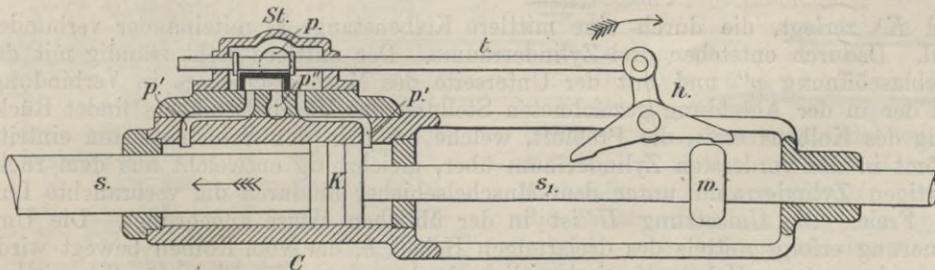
Prinzipskizze. Steuerung der Bohrmaschine Rud. Meyer, ältere Bauart.
